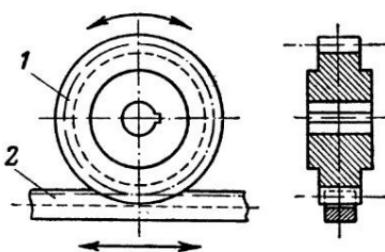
Реечное зацепление: 1 — зубчатое колесо; 2 — зубчатая рейка.
